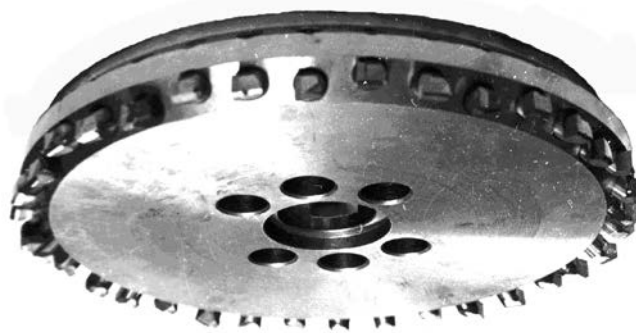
Фреза Ø315 мм для чернового торцового фрезерования плоских поверхностей столов машин
